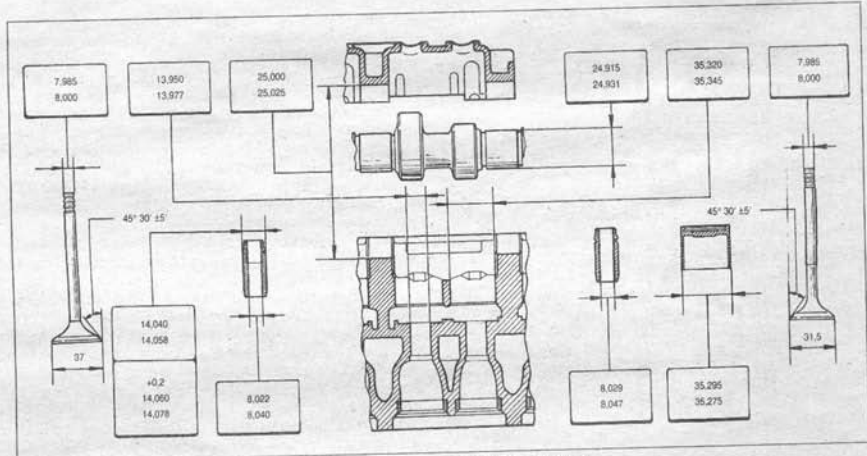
Основные размеры головки цилиндров и деталей механизма привода клапанов
